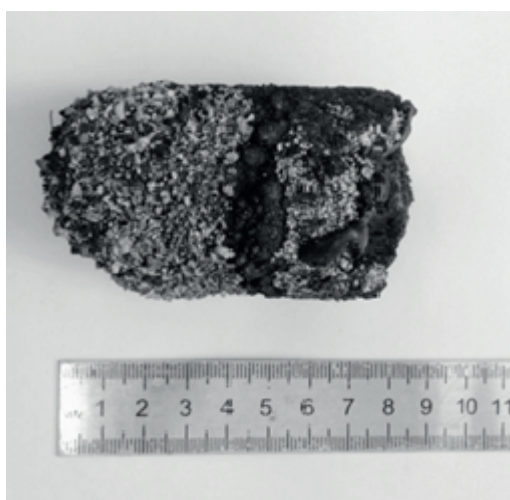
Образец, изготовленный на электрошлаковой установке без удаления шлака
